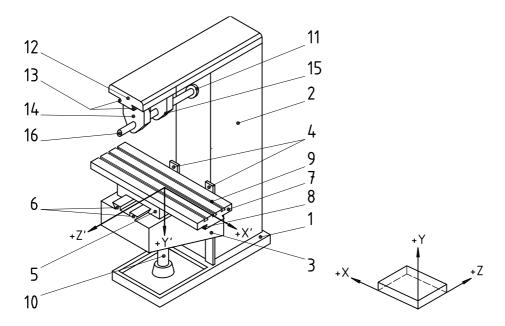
Machines à fraiser à table à hauteur variable, à broche horizontale fixe
